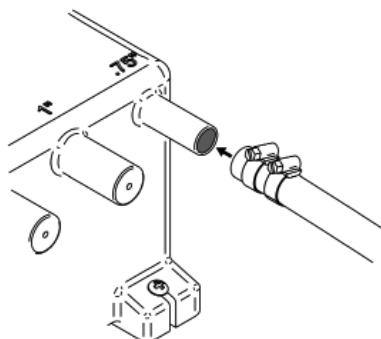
Gulper 220 - pumpun kääntyvä pää
